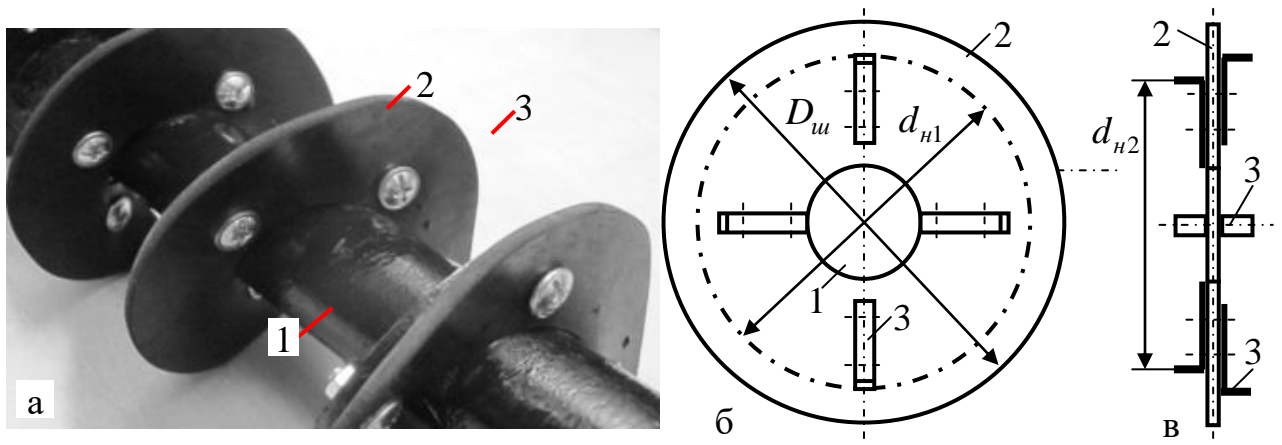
Схема розміщення Г-подібних ножів-подрібнювачів на спіральному витку шнека: 1 – барабан шнека; 2 – спіральний виток; 3 – Г-подібний ніж-подрібнювач; а – загальний вигляд; б – вигляд збоку; в – вигляд спереду
